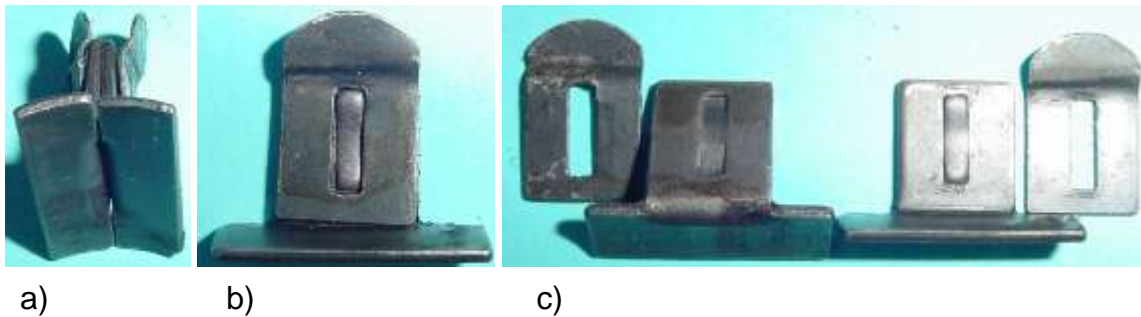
Pol mit Spulenkern: a) Gesamtansicht, b) Ineinander gefügtes Blechpaar, c) Einzelteile des Pols
